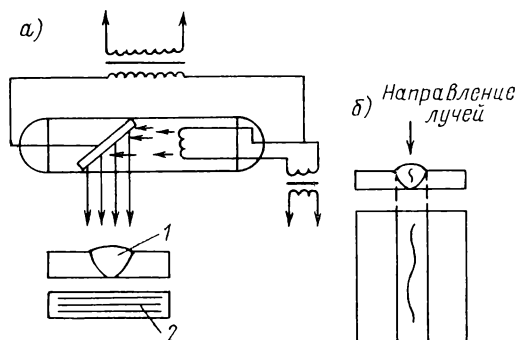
Схема рентгеновского контроля сварного соединения: а — схема рентгеновской трубки; б — рентгенограмма сварного соединения.
